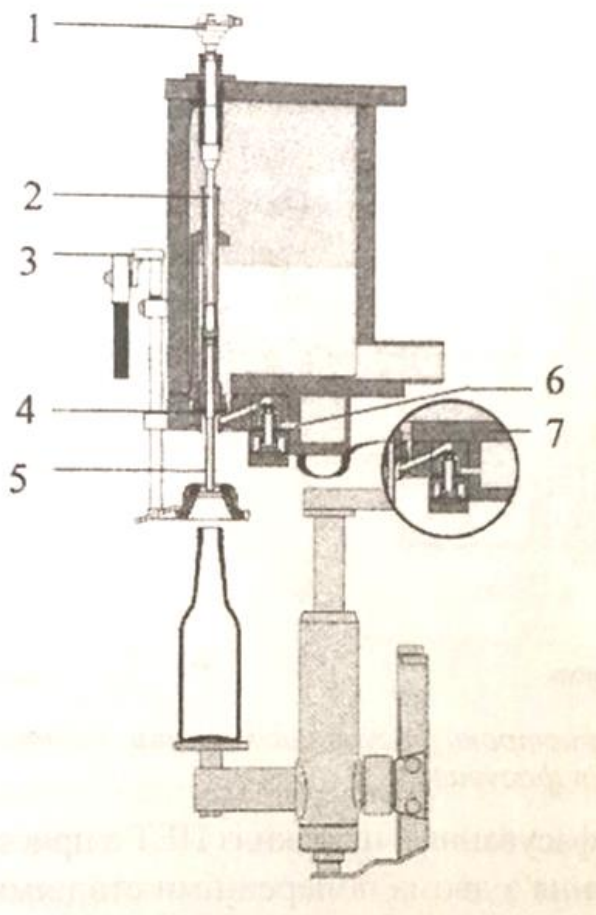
Пристрій фасування машини Mecafill VKP: 1- керування роботою рідинного клапана; 2- трубка подачі газу; 3- ролик кулачкового механізму; 4— затвор для газу; 5- трубка відведення повітря 6— канал SIP; 7 — розвантажувальний вентиль ;
